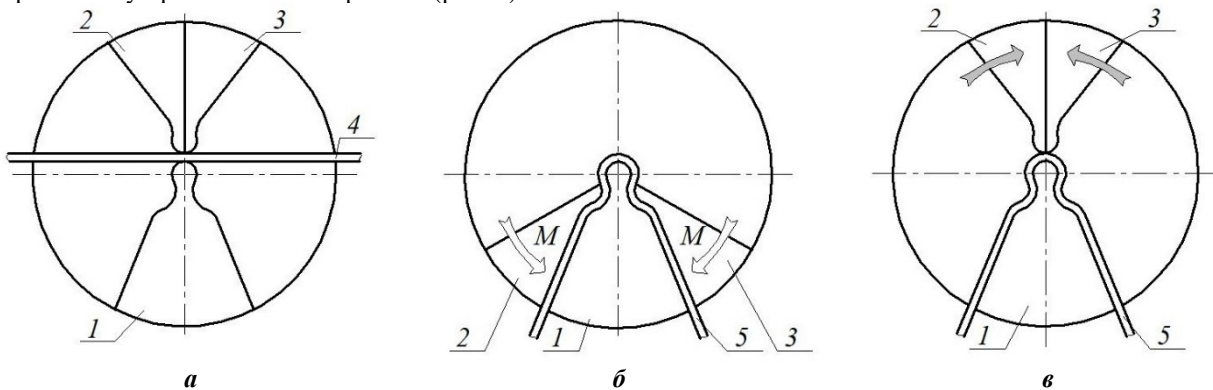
Спосіб виготовлення V-подібної пружини муфти пружної: а) – заготовка закріплена на матриці; б) – формування V-подібного профілю пружини; в) – пружина готова до демонтажу
